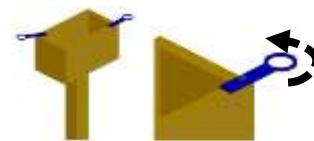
ELEMENTO CON EJE CENTRAL PARA EVITAR CABLES EN EL EXTERIOR.
